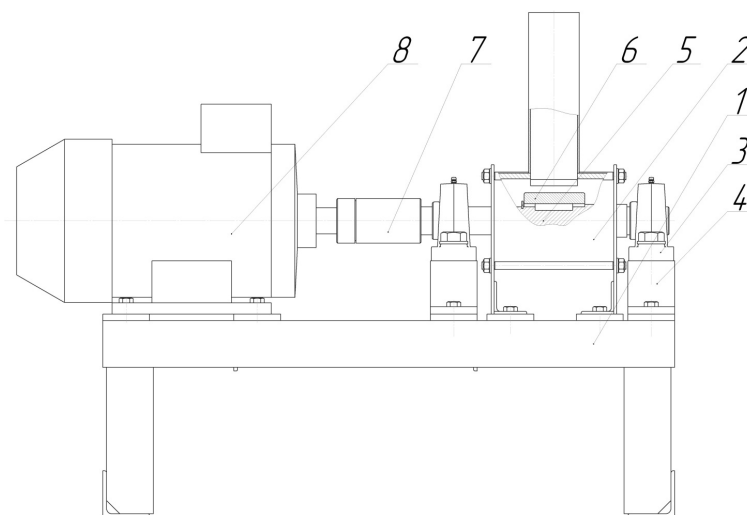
Общий вид дымогенератора: 1 – основание; 2 – корпус; 3 – подшипники; 4 – подставки для подшипников; 5 – вал; 6 – фрикционный диск; 7 – муфта; 8 – электродвигатель
